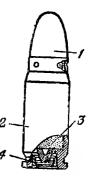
Боевой патрон: 1 — пуля; 2 — гильза; 3 — заряд; 4 кансколь
